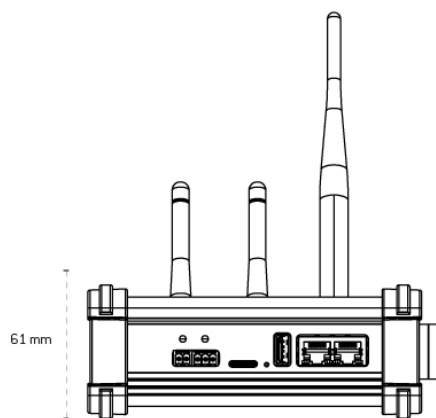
Dimensões do Universal IoT Gateway com caixa de alumínio
